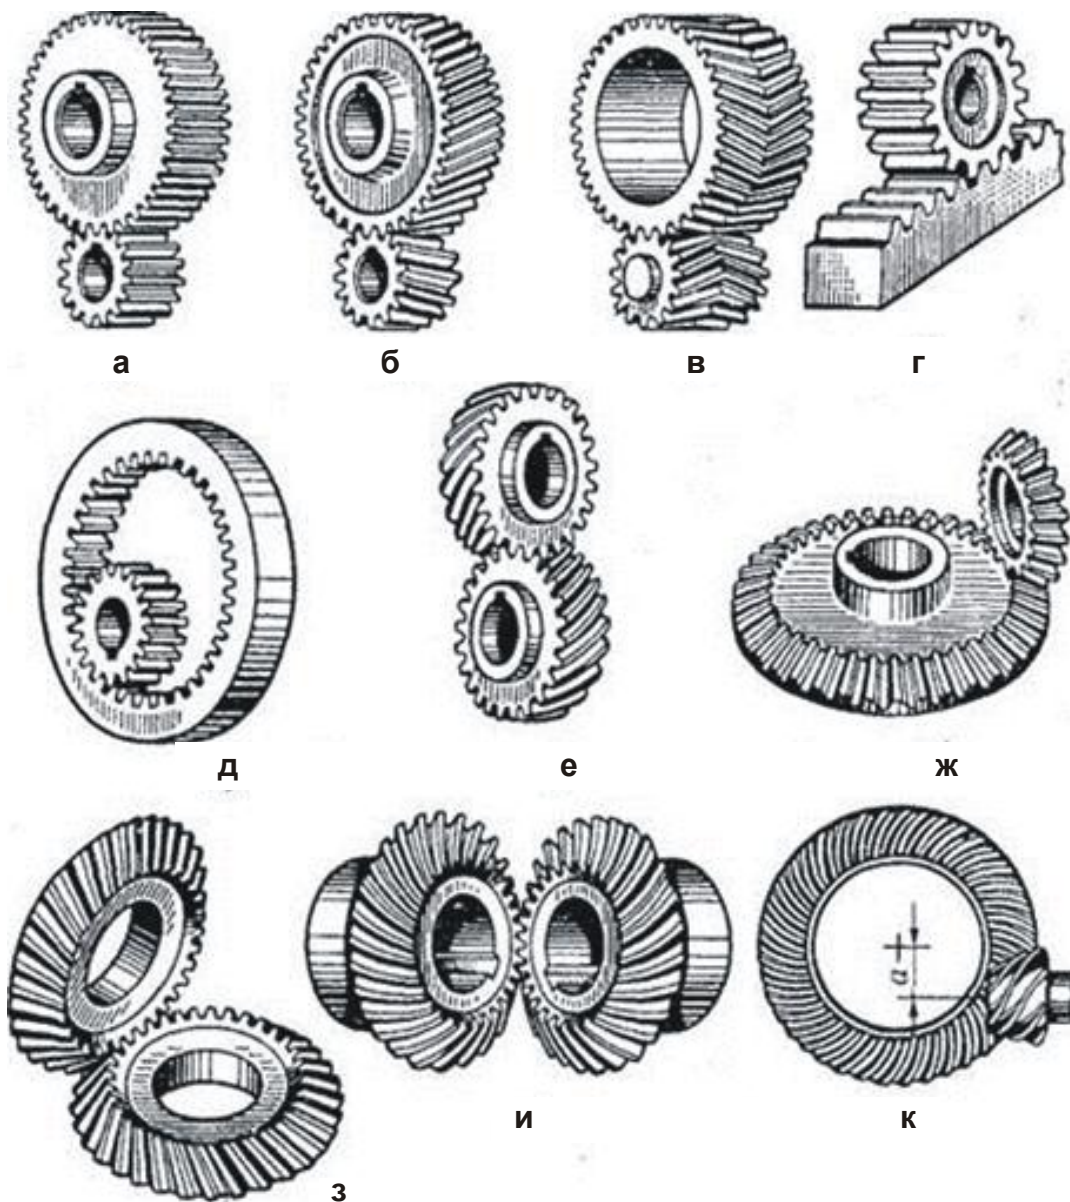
Види зубчастих передач: а, б, в – циліндричні зубчасті передачі із зовнішнім зачепленням; г – рейкова передача; д – циліндрична передача із внутрішнім зачепленням; е – зубчаста гвинтова передача; ж, з, и – конічні зубчасті передачі; к – гіпоїдна передача
